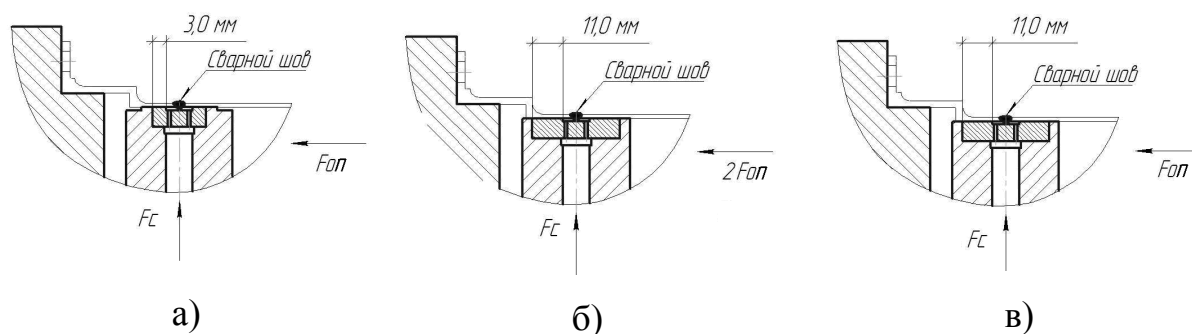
Варианты закрепления сварного изделия в приспособлении
